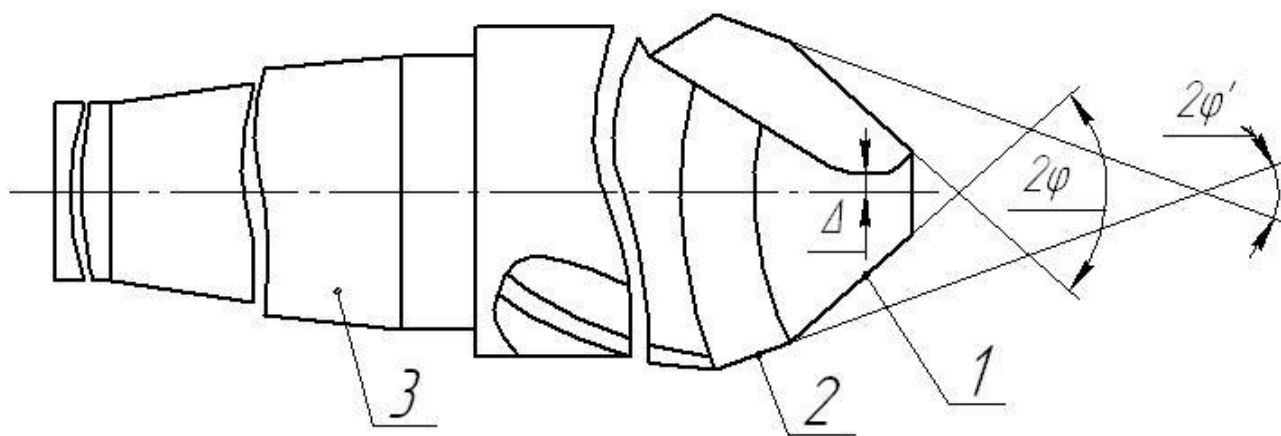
Схема разработанного спирального сверла с режущей частью со сдвоенной заточкой
